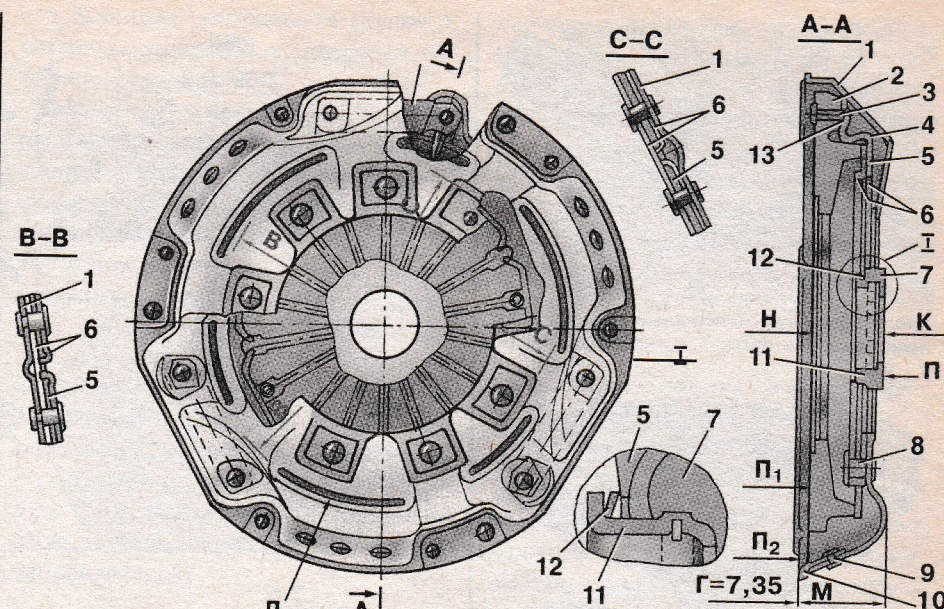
Нажимной диск сцепления с кожухом в сборе: 1 — кожух сцепления; 2 — нажимной диск; 3, 9 — заклепки; 4 — соединительное звено; 5 — нажимная пружина; 6 — стопорное кольцо; 7 — опорная пята; 8 — стяжной палец; 10 — балансировочный грузик; 11 — центральная втулка; 12 — пружинное коническое кольцо; 13 — соединительная пластина
